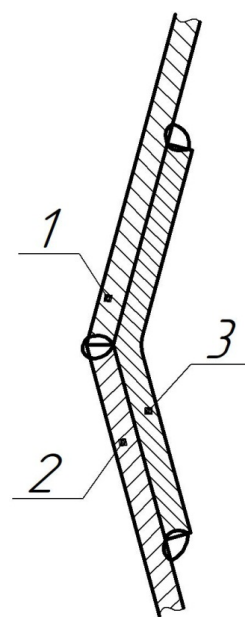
Схема приварки усилителей при сборке кузовов автомобилей:
